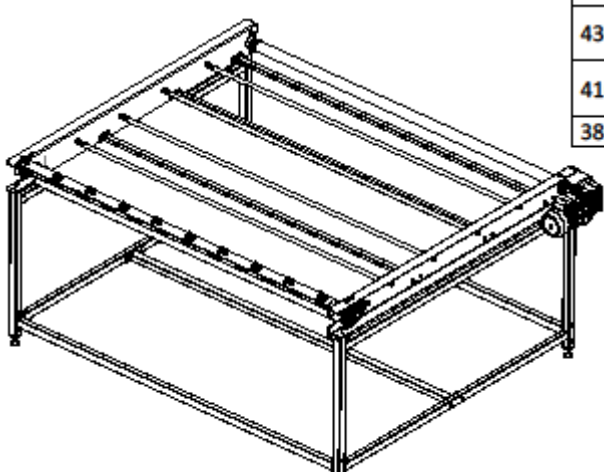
Desenho técnico do conjunto suporte lateral direito e extras (6601).
